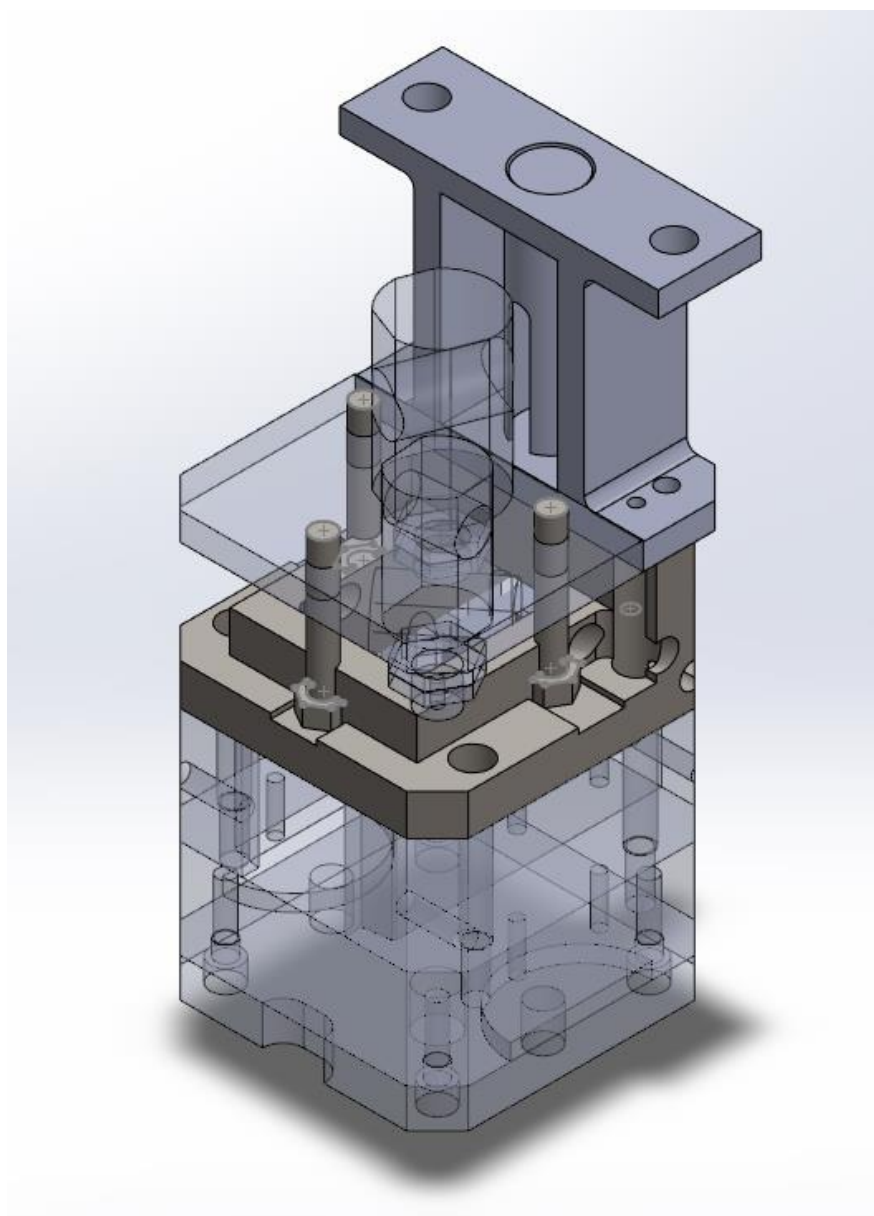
Mecanismo de *Quick-Stop*, vista frontal
